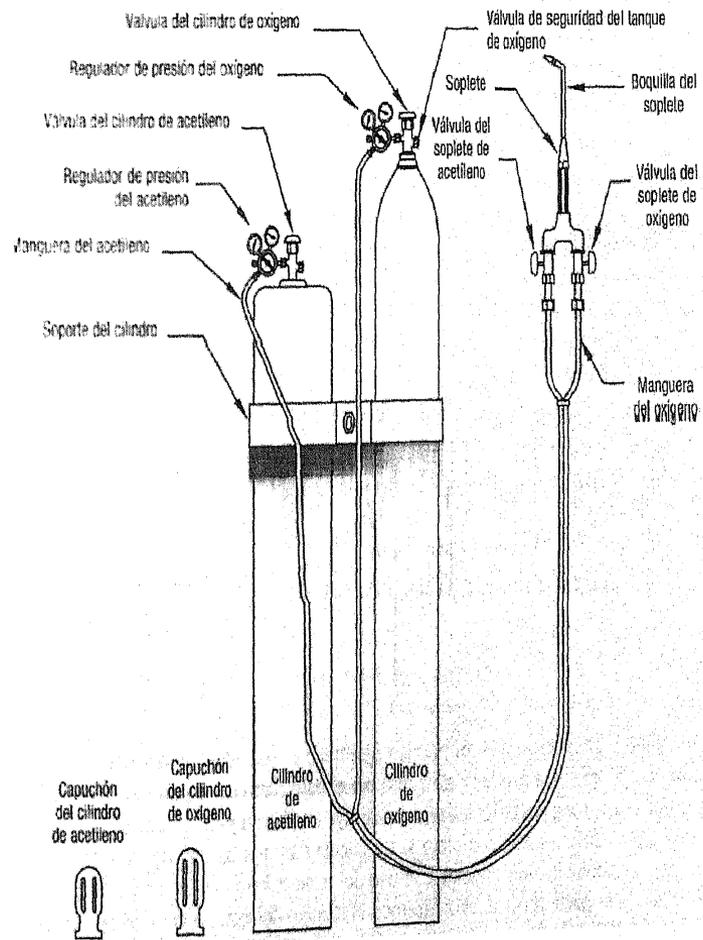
Equipo para soldadura de Oxiacetileno.
